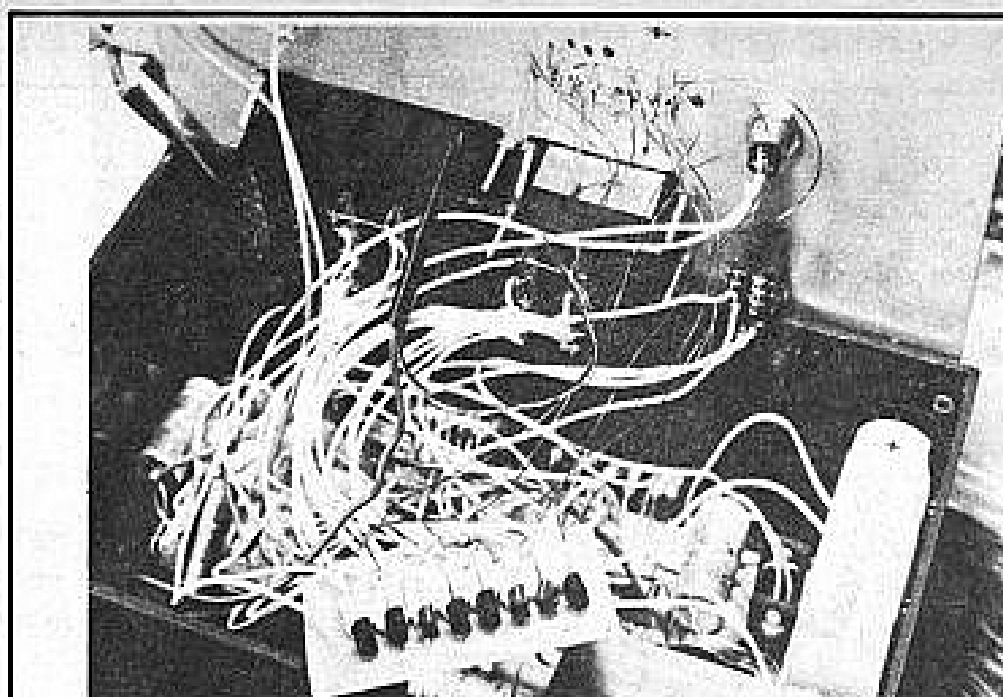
Trois techniques ont été employées pour le câblage : le circuit imprimé (visu-données), la plaquette à trous pour assemblage sans soudure et le wrapping (les LEDs de la visu). Visibles à droite : les deux régulateurs de tension d'alimentation + 5, - 6.
